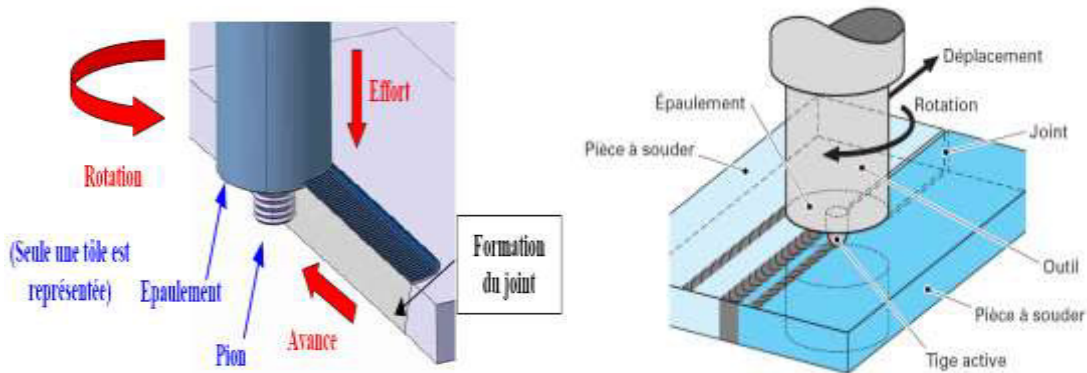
Principe du soudage par Friction-Malaxage (FSW).
